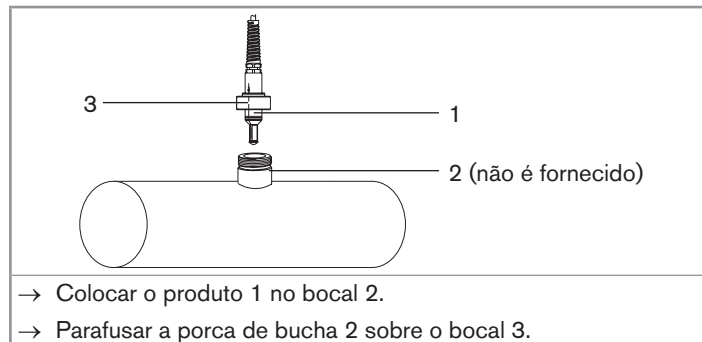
Instalação de um 8221 com conexão G1 1/4" em uma tubulação
